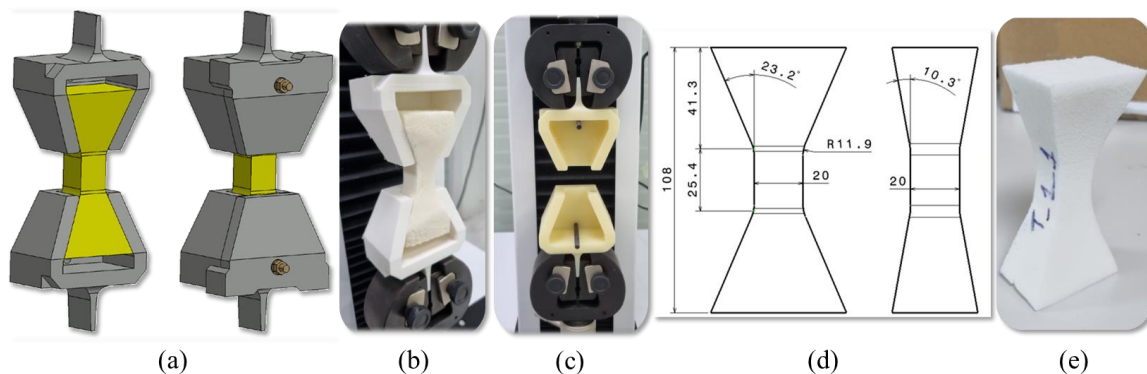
Dispositivo de fixação: (a) Projeto 3D, (b) Protótipo em impressão 3D, (c) Dispositivo final usinado em ABS, (d) Dimensional da amostra, (e) Amostra (2022)
